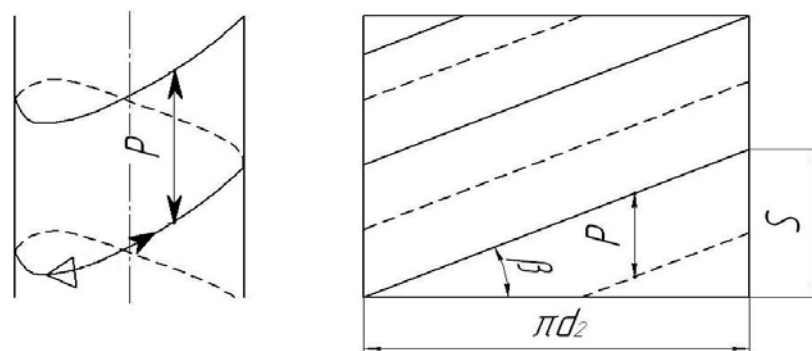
Образование резьбы, развёртка винтовых линий двухзаходной резьбы
